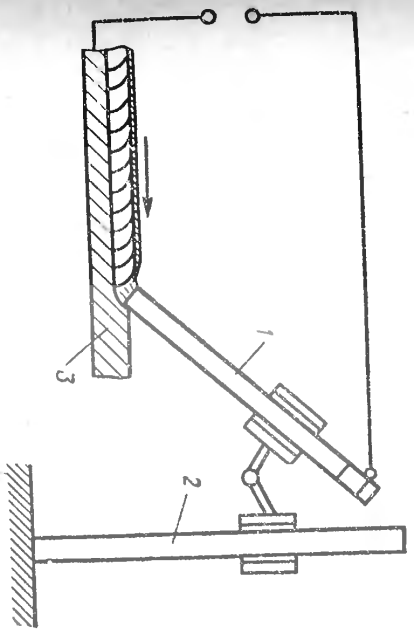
Схема сварки наклонным электродом с постоянным углом наклона: 1 — электрод, 2 — стойка, 3 — свариваемая заготовка
